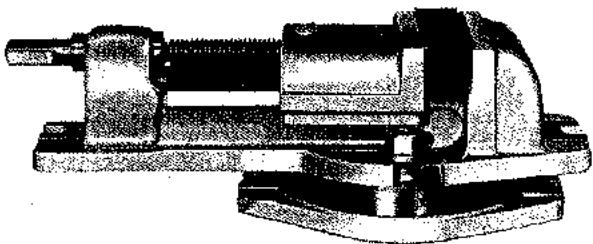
Tornillo de mordazas giratorio (Cincinnati Milling Machine Co.)
